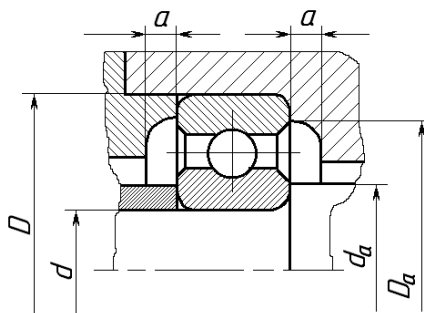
Размеры заплечиков для шарикоподшипников по ГОСТ 8338
